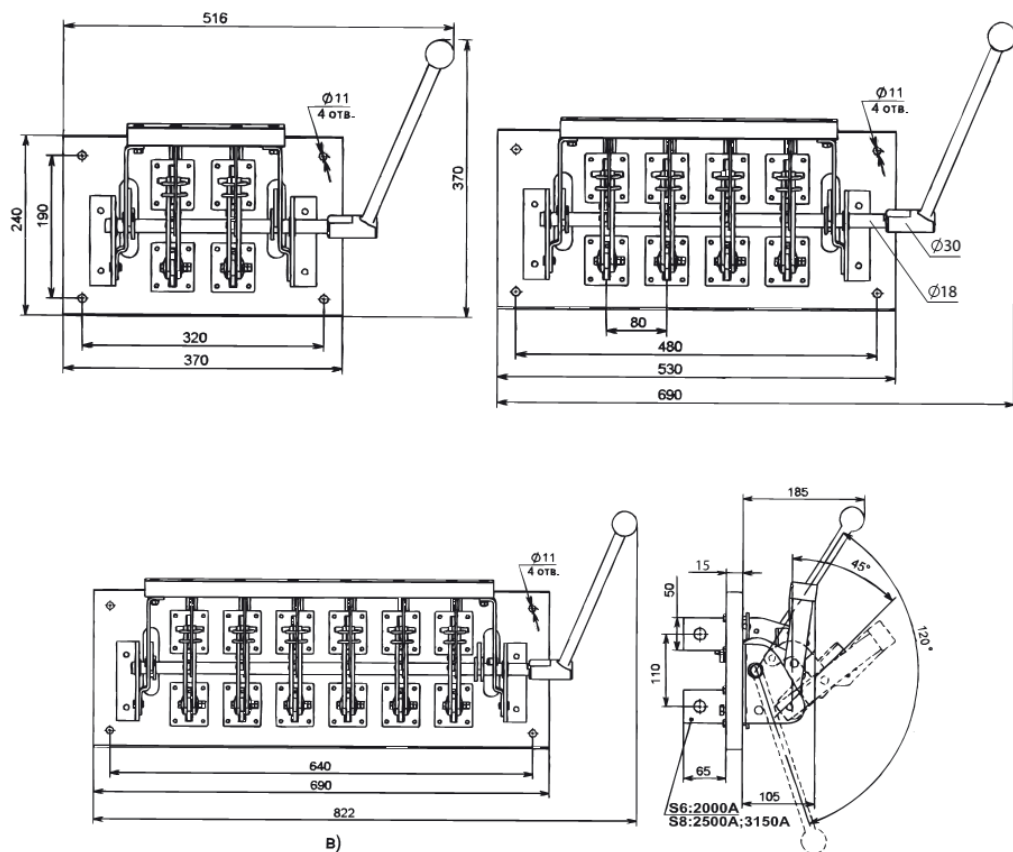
Разъединитель РЕ19 с боковой смещенной рукояткой
